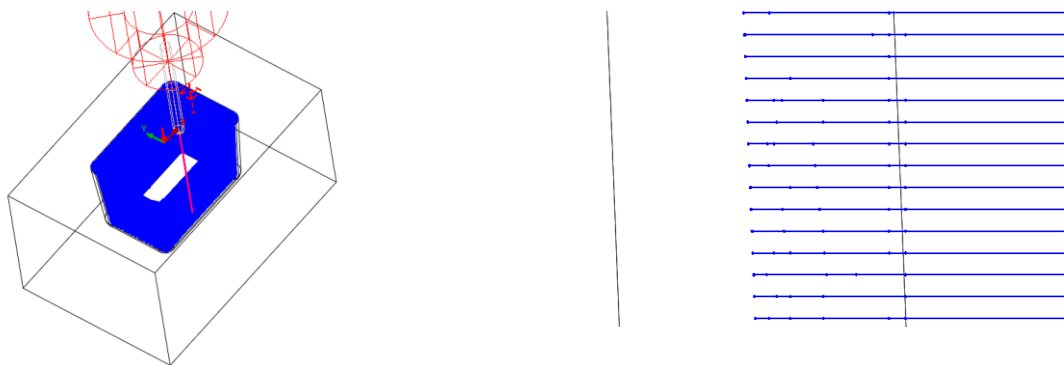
Траєкторія руху інструмента при чистовому фрезеруванні нахилених стінок призматичного заглиблення
